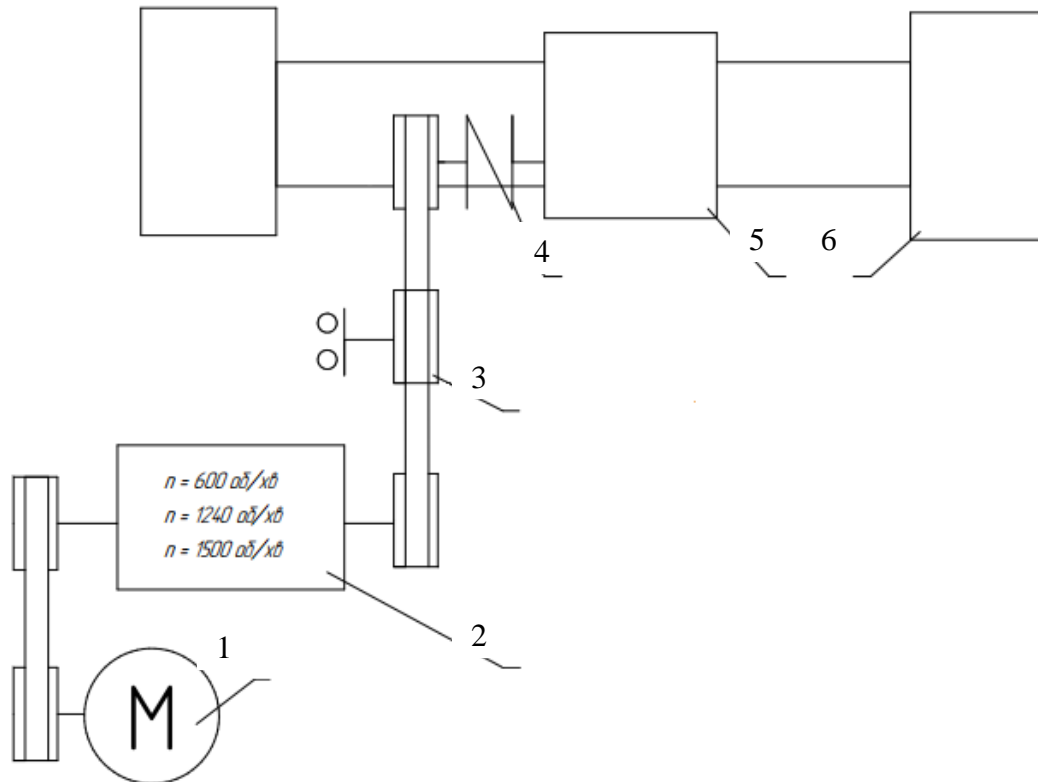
Кінематична схема стану обкатки ведучих мостів комбайнів: 1 – електродвигун; 2 – коробка передач; 3 – натяжний ролик; 4 – Муфта; 5 – коробка діапазонів; 6 – ведучий міст.
